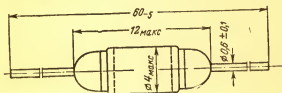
Габаритный чертеж диодов Д219А—Д220Б.
